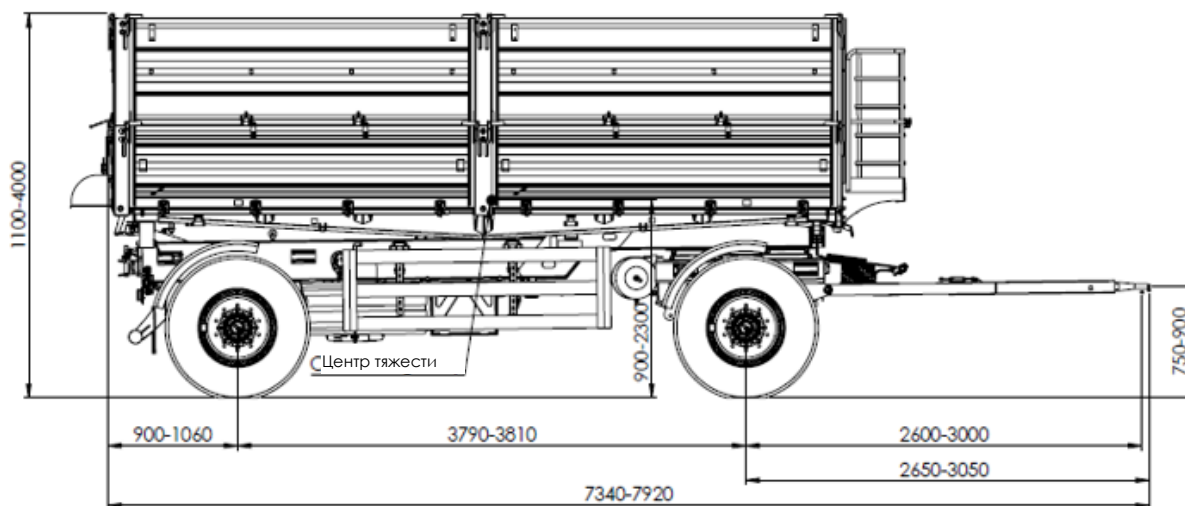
Размеры прицепа Т739А - вид сбоку
